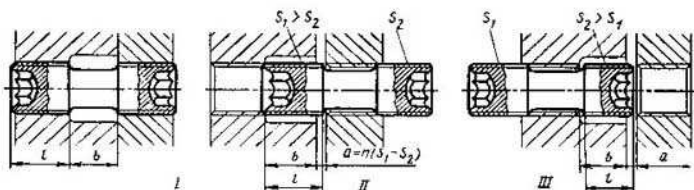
Unión de piezas mediante un tornillo con rosca diferencial: *I* y *II*—posiciones después y antes del montaje; *III*—variante de montaje
